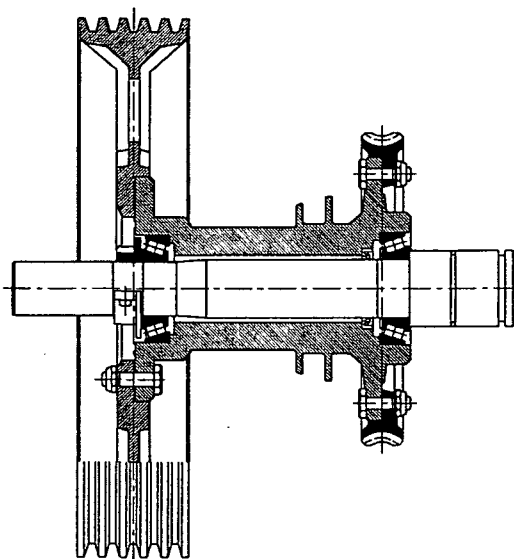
Червячное колесо и тяговый шкив общей ступицей
